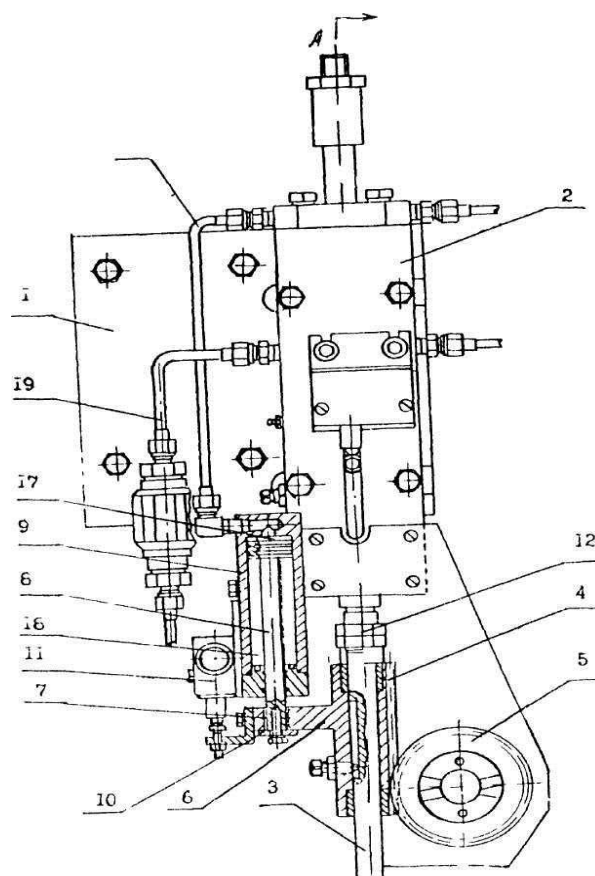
Привод подачі шпindelної головки свердлувального верстата
